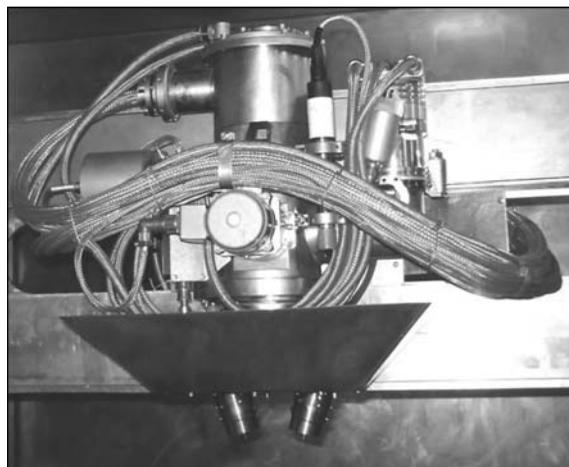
Общий вид внутрикамерной сварочной электронной пушки с ускоряющим напряжением 60 кВ и мощностью пучка 60 кВт
